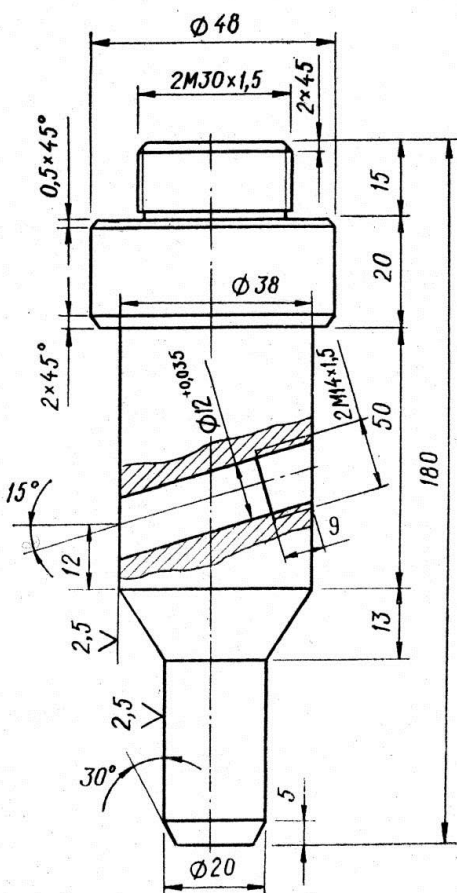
Різцева оправка для обробки фасок клапанних гнізд головки циліндрів.
